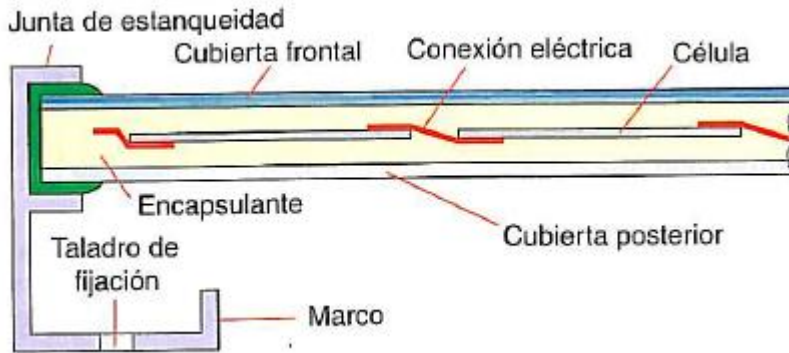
Detall seccionat de l'estructura d'un mòdul fotovoltaic (Font: Castejón et al., 2010).
